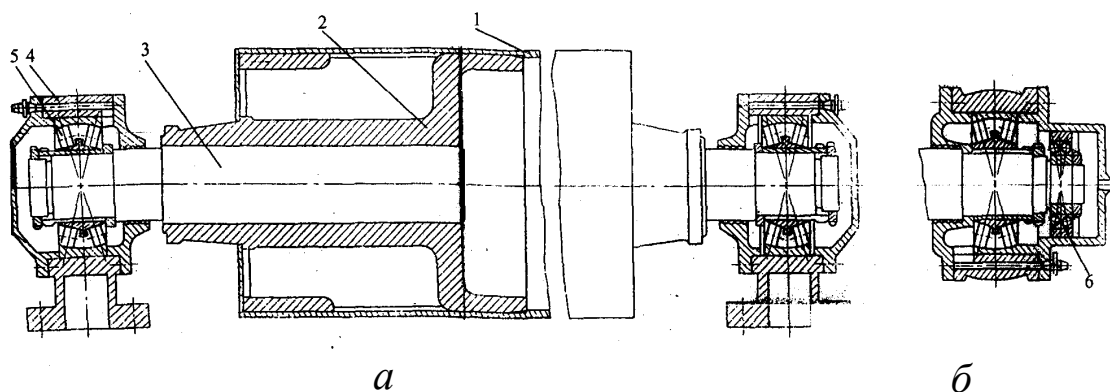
Трубчатый вал: *а* – с корпусами подшипников в виде стоек; *б* – со сферическими корпусами подшипников: 1 – труба; 2 – патрон; 3 – цапфа; 4 – корпус подшипника; 5 – подшипник; 6 – концевой подшипник
